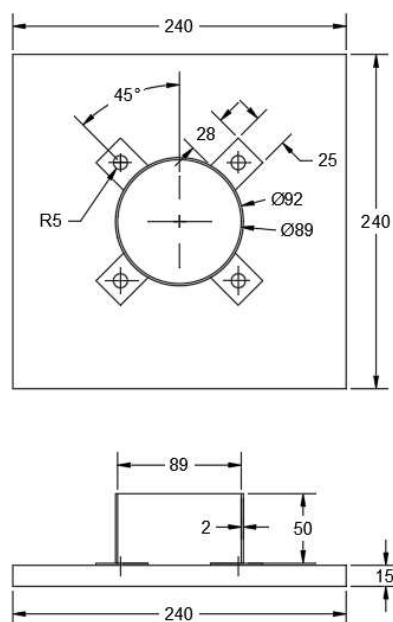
30 - Suporte base para ensaio de flexão com engaste da pá.
